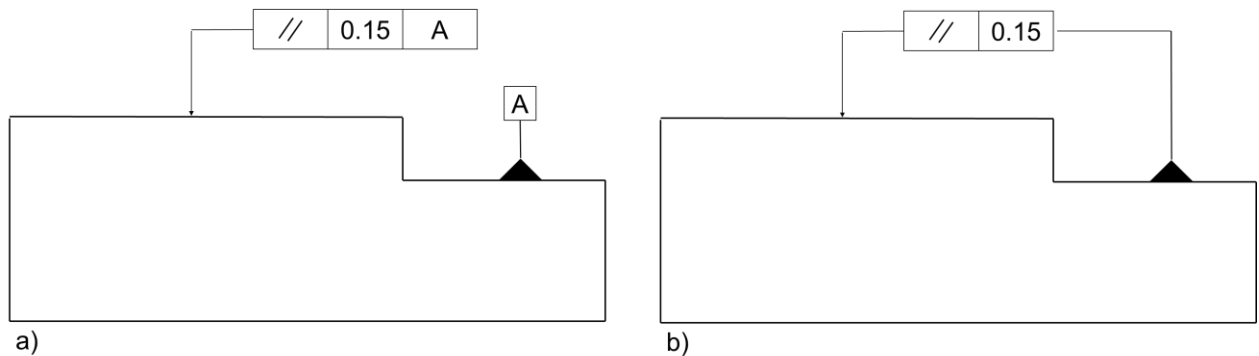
a) Tolerancia geométrica con datum A de referencia b) Tolerancia geométrica con la referencia unida directamente al rectángulo de tolerancia
